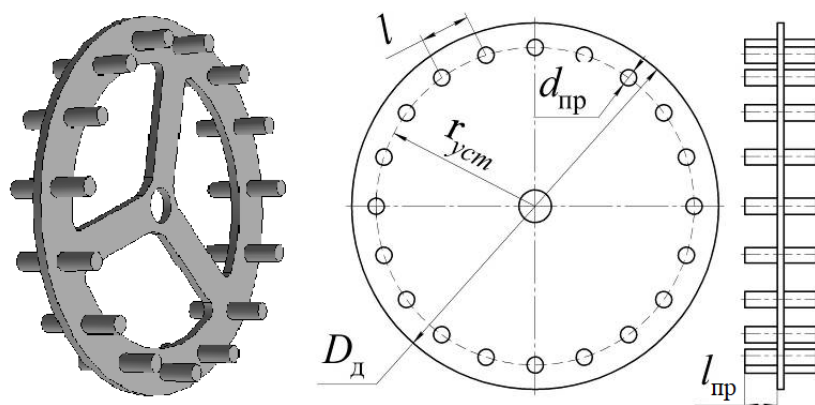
Общий вид и основные параметры кольчато-пруткового катка
